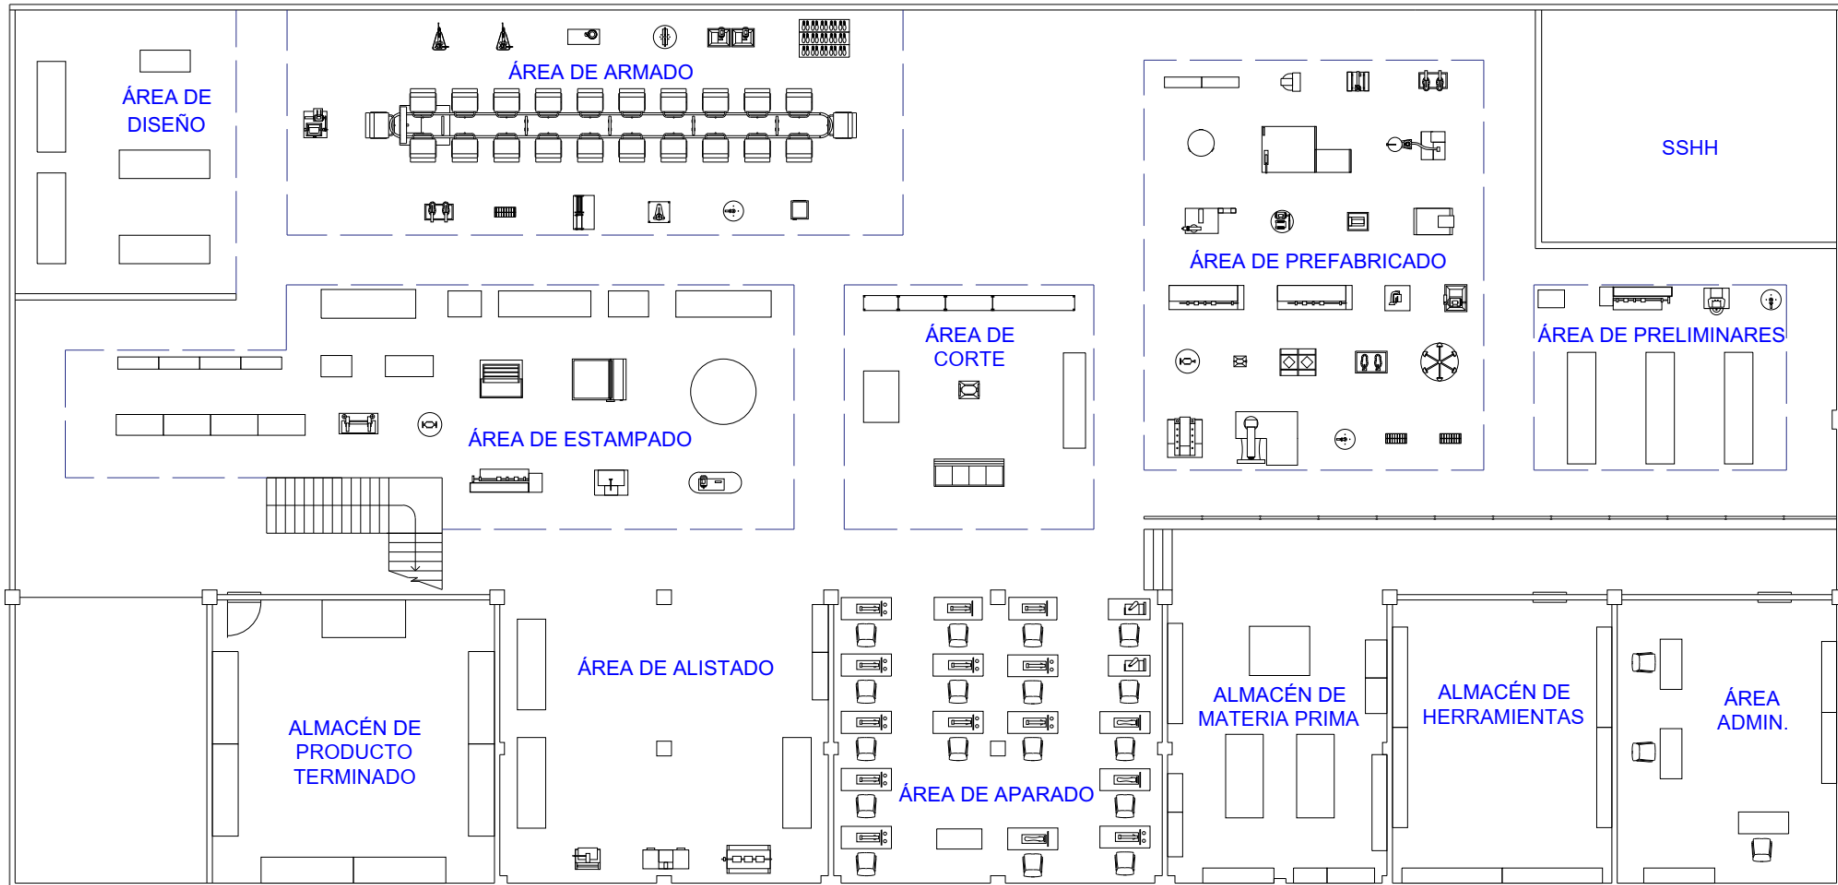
Redistribución de Planta a Detalle. Fuente: Elaboración Propia.
